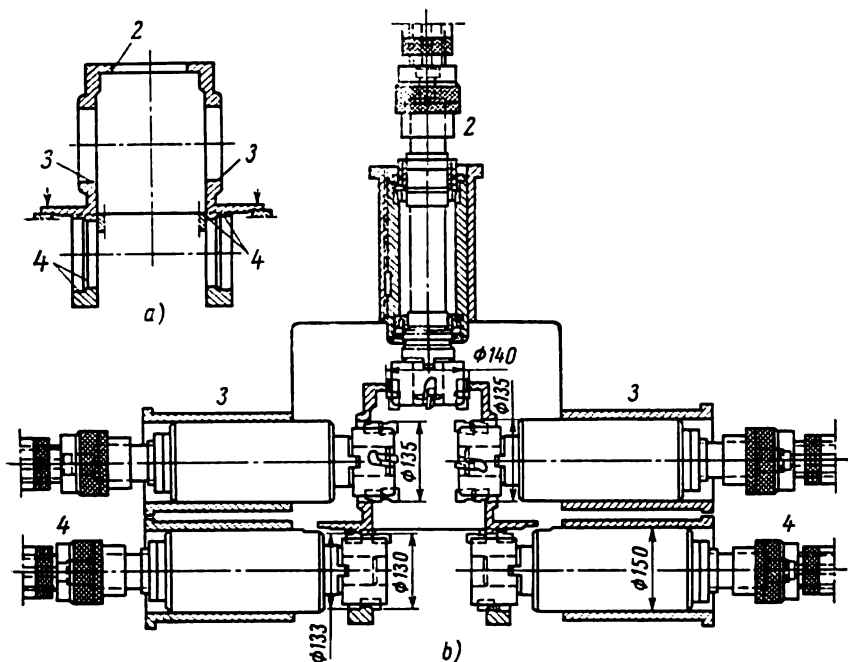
Exemple de réglage pour l'usinage d'un carter de démultiplicateur sur une machine à unités d'usinage assurant le façonnage simultané des trois côtés:
